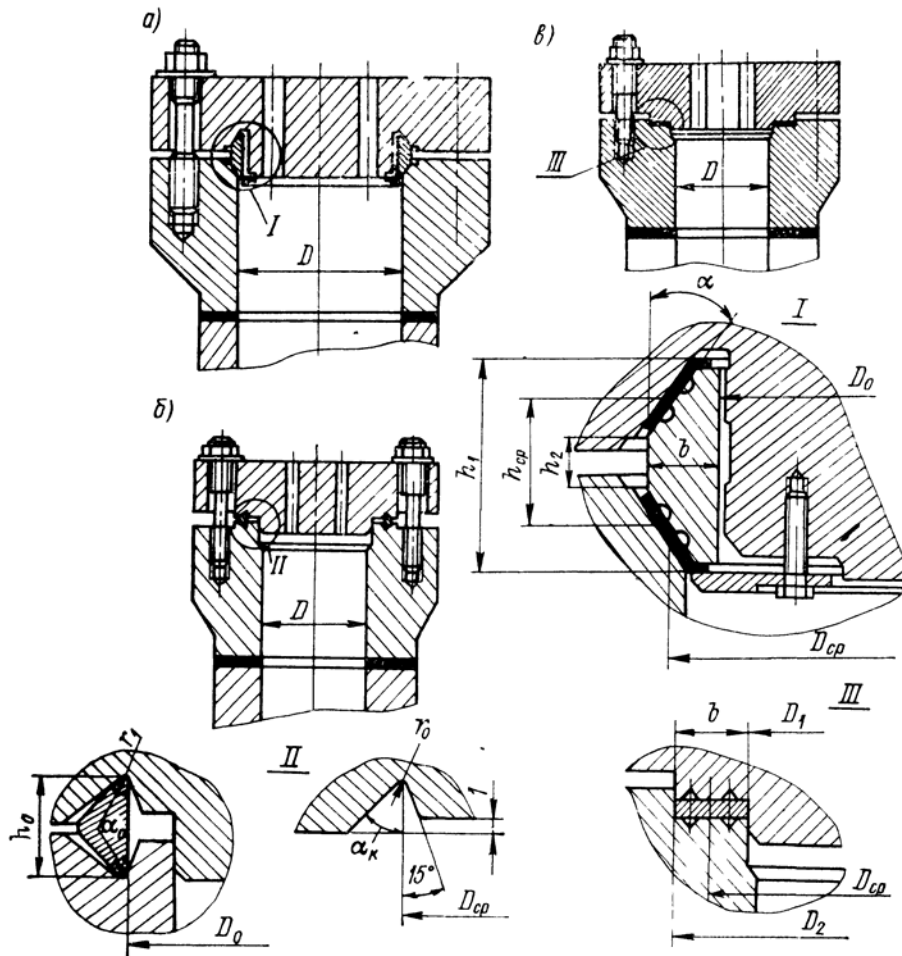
Конструкции затворов: а – с двухконусным obturatorом; б – с дельта-obturatorом; в – с плоской металлической прокладкой.
